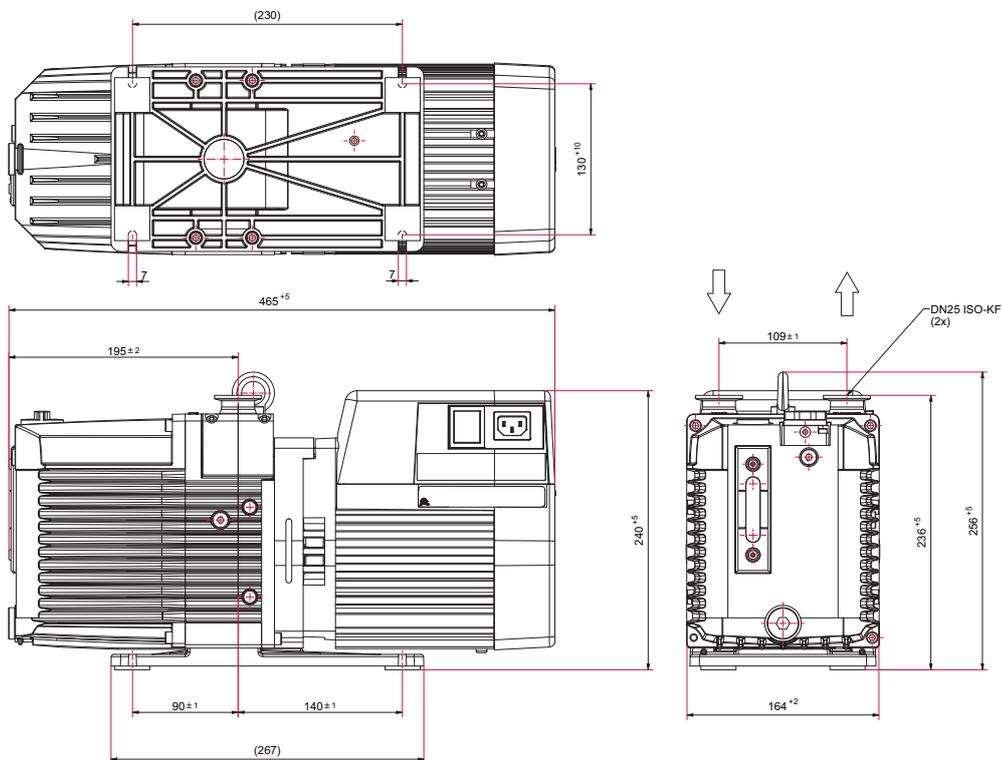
Abmessungen DuoVane 18 mit Einphasenmotor
